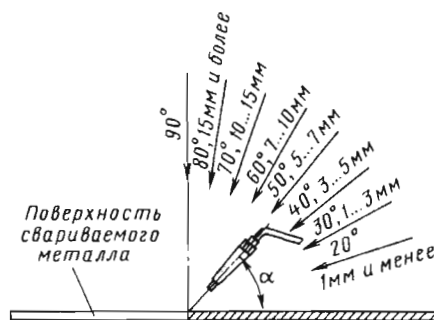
Углы наклона мундштука горелки при сварке стали разных толщин
